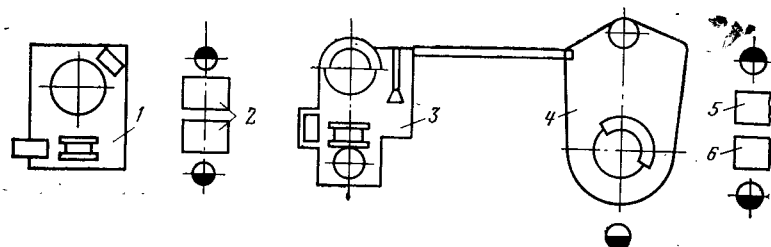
Схема планировки оборудования линии сборки минитюрных ламп с механизированным монтажом тела накала.
